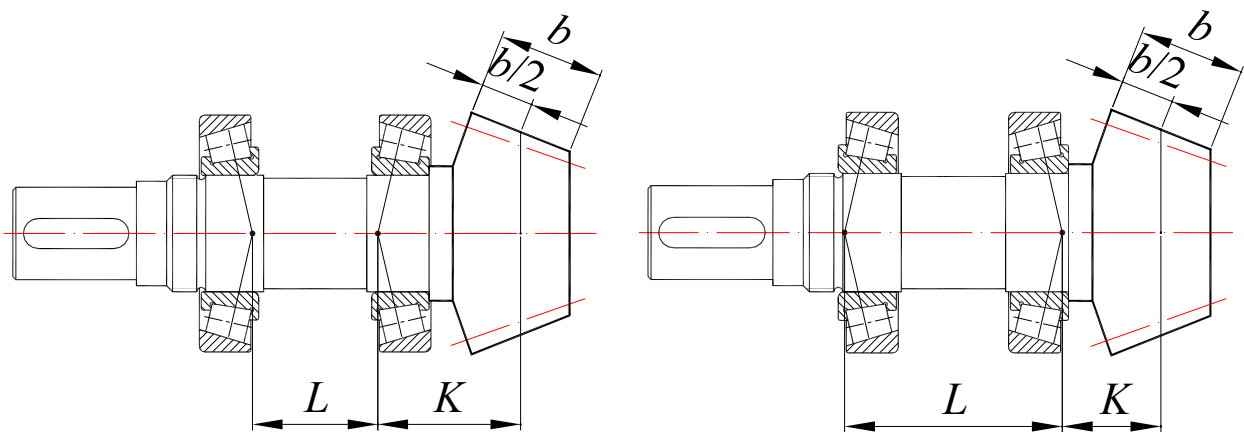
Другий етап ескізного компонування конічно-циліндричного редуктора
